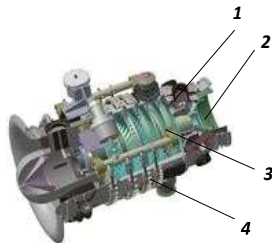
Осевий компресор: 1 – корпус; 2 – ротор; 3 – лопатки; 4 – напрямний механізм
